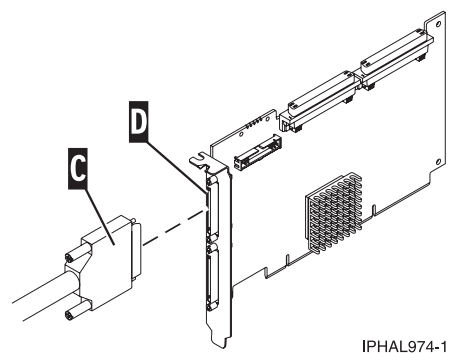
Cable SCSI a una targeta d'interfície SCSI
